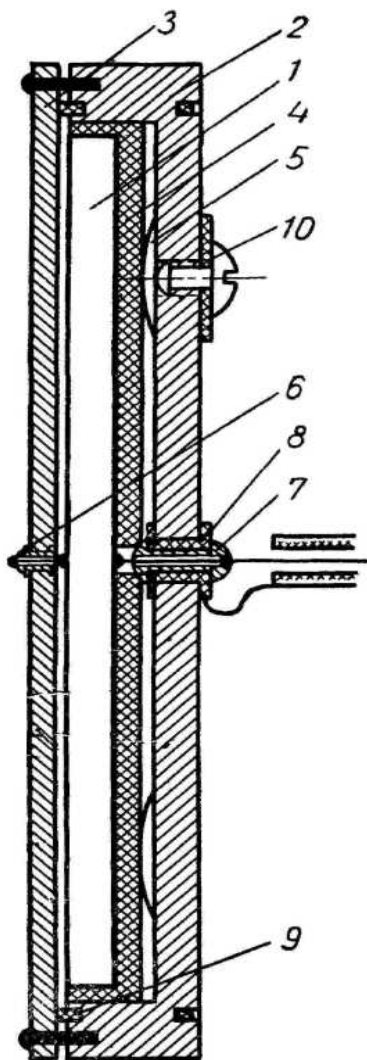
1 — пластина из титаната бария; 2 — корпус; 3 — передняя стенка; 4 — пенопластовый чехол; 5 — пружина; 6 — взвод; 7 — стержень; 8 — изолятор; 9 — прокладка; 10 — винт - пробка
